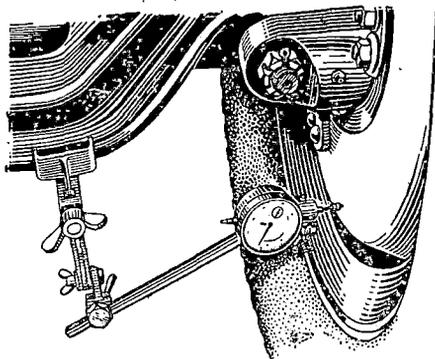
Прибор для проверки зазоров в шкворневых соединениях без разборки переднего моста
